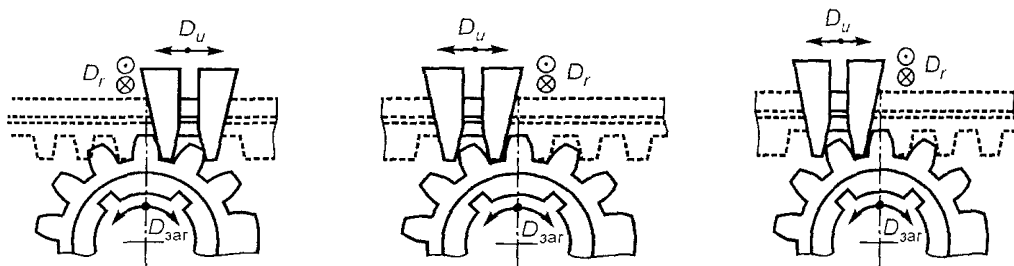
Нарезание конических зубчатых колес с прямыми зубьями
